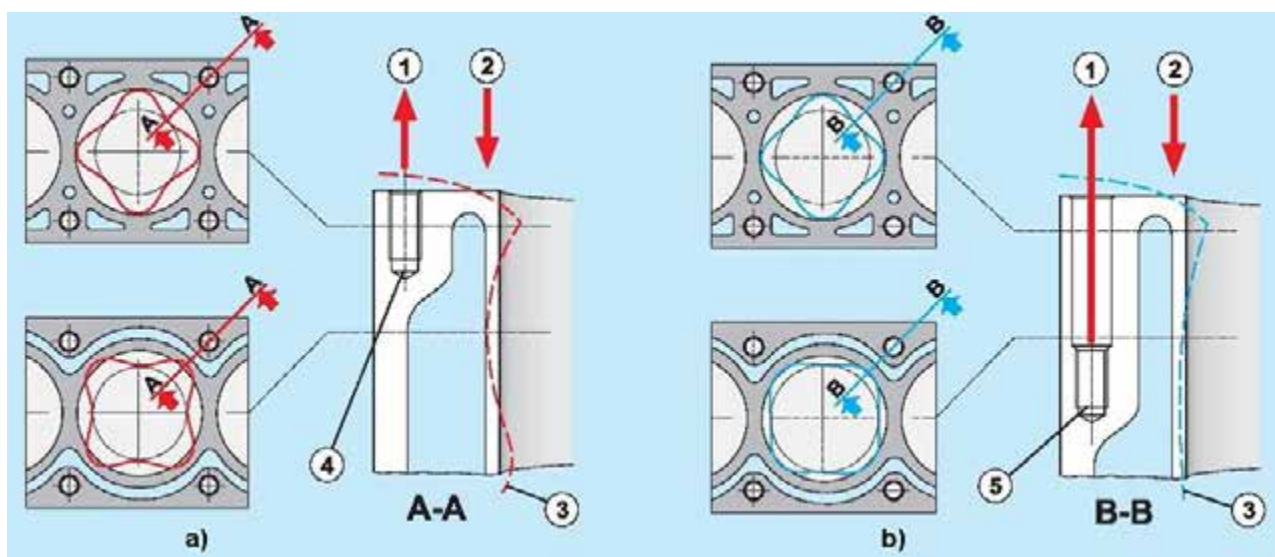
ro-20: Сравнительная оценка деформации цилиндра при различном исполнении резьбовых отверстий крепления головки цилиндров; источник: MSI
